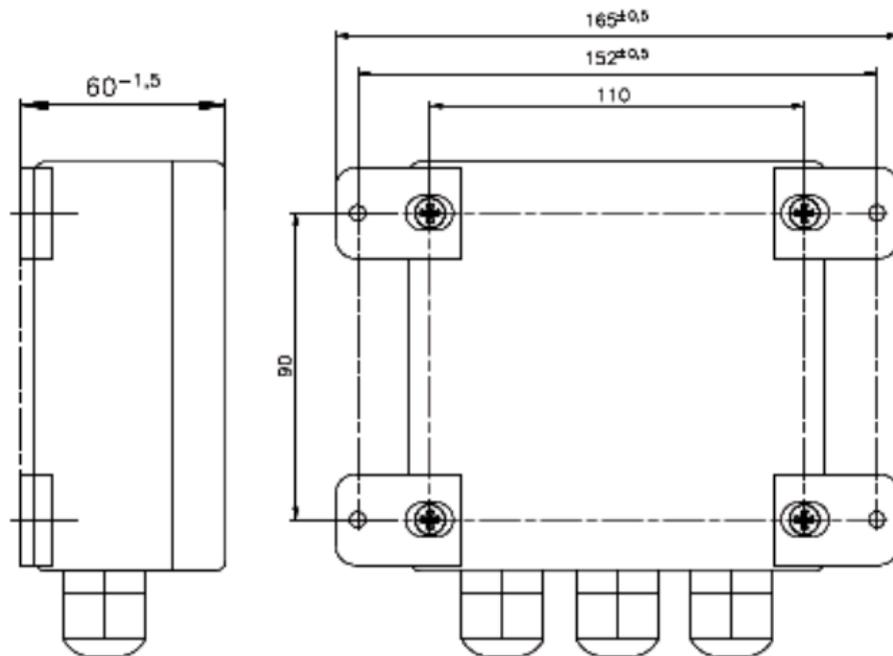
Габаритные размеры для крепления корпуса типа К1 с пластиковыми кронштейнами
